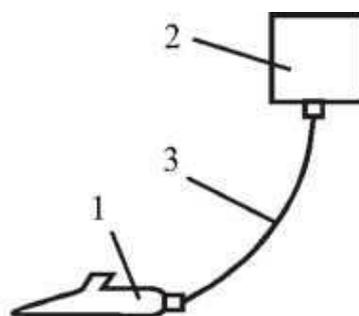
Схема агрегата ЭСА-1Д
